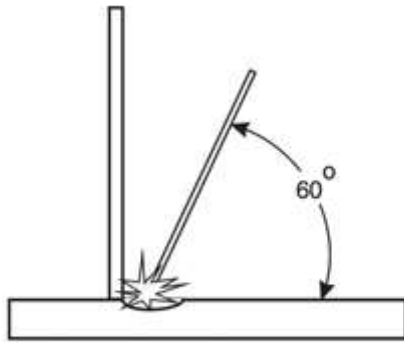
Сварка тонкого с более толстым металлом.
